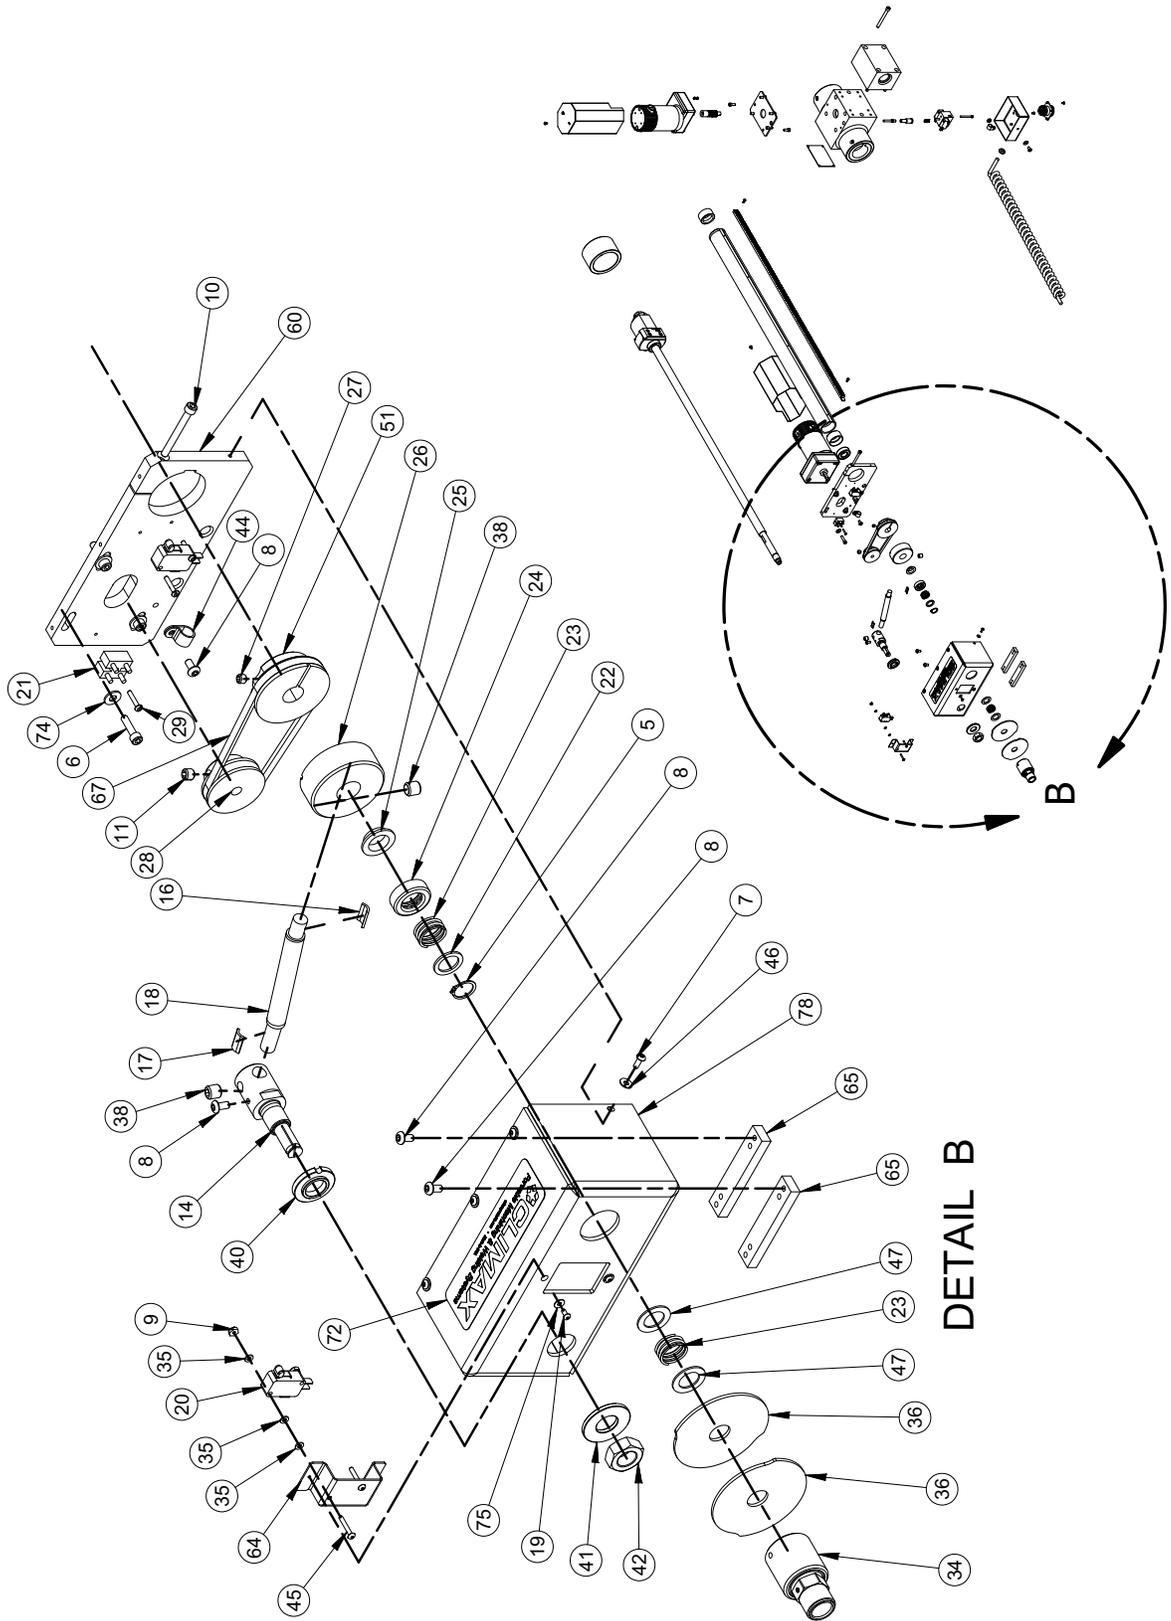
ENSEMBLE DE TÊTE DE SOUDAGE 2(RÉF. 91808)
